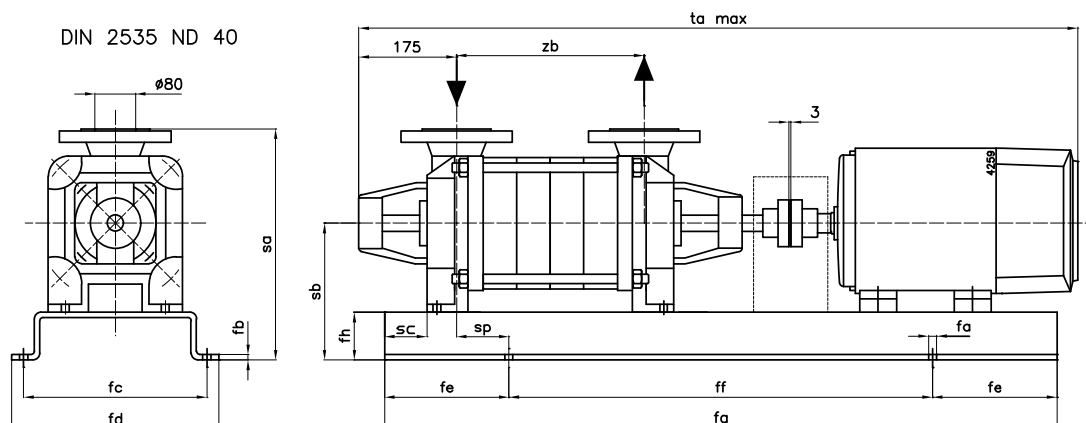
Dimensions ensemble moto-pompe MCH(S)(W) 20a.
